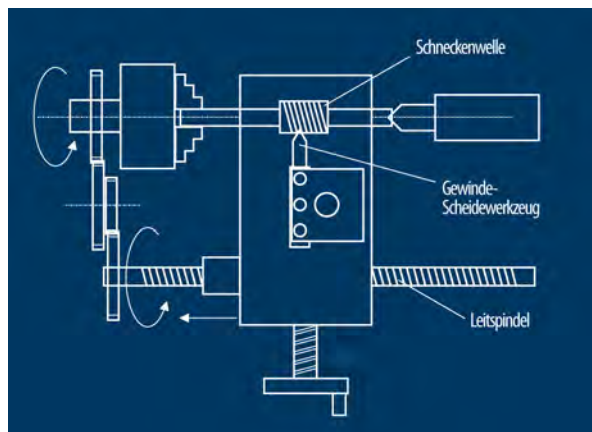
Zur Gewindeherstellung mit der Drehmaschine wird das Schneidwerkzeug mittels einer Leitspindel in Längsrichtung bewegt. Verschiedene Gewindesteigungen erhält man durch Verändern des Übersetzungsfaktors zwischen Werkstück- und Leitspindeldrehung.
